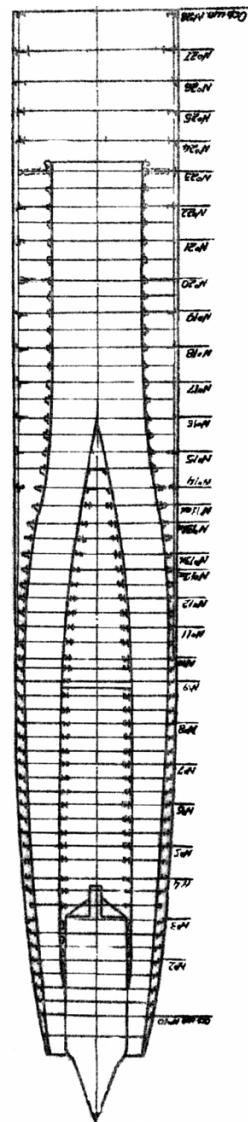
Общий вид воздушного канала (вид сверху)
